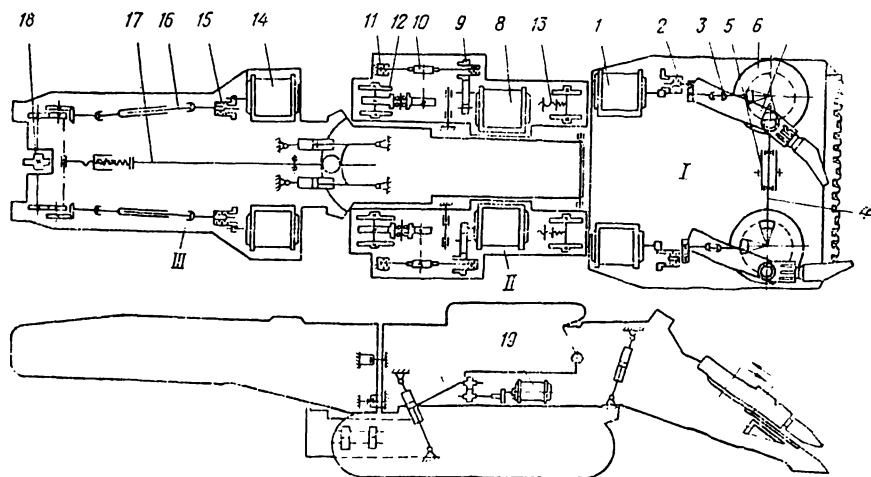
Кинематическая схема машины «Джой 19NR» и ПНБ-3К с нагребающими лапами и индивидуальным приводом:
